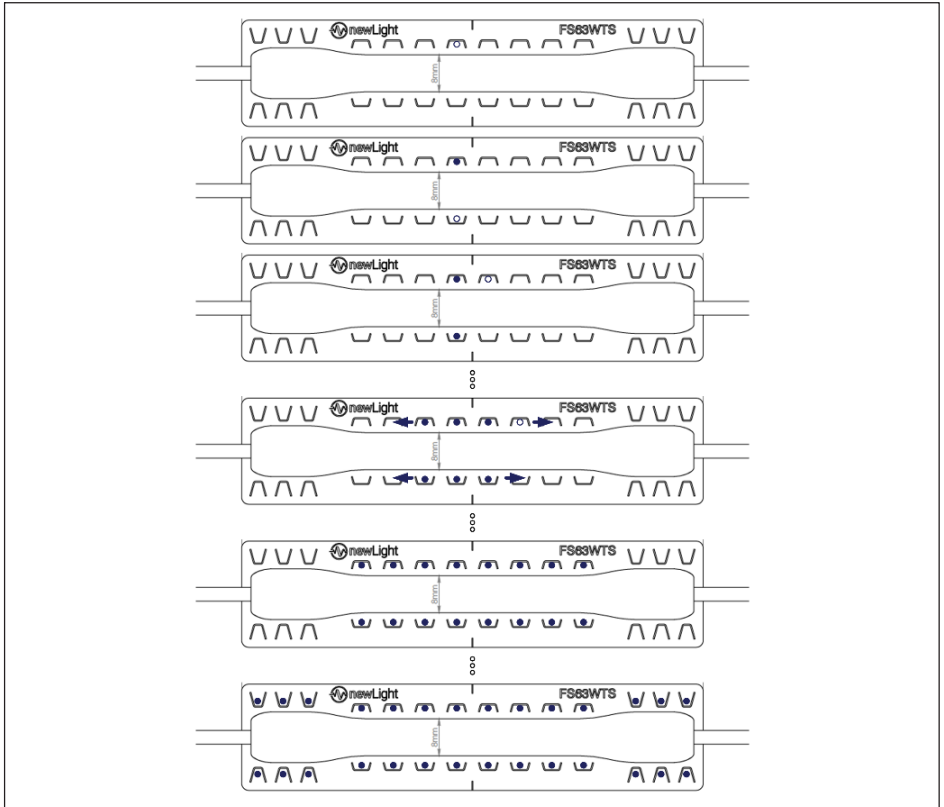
Parcours de soudage du FS63WTS
